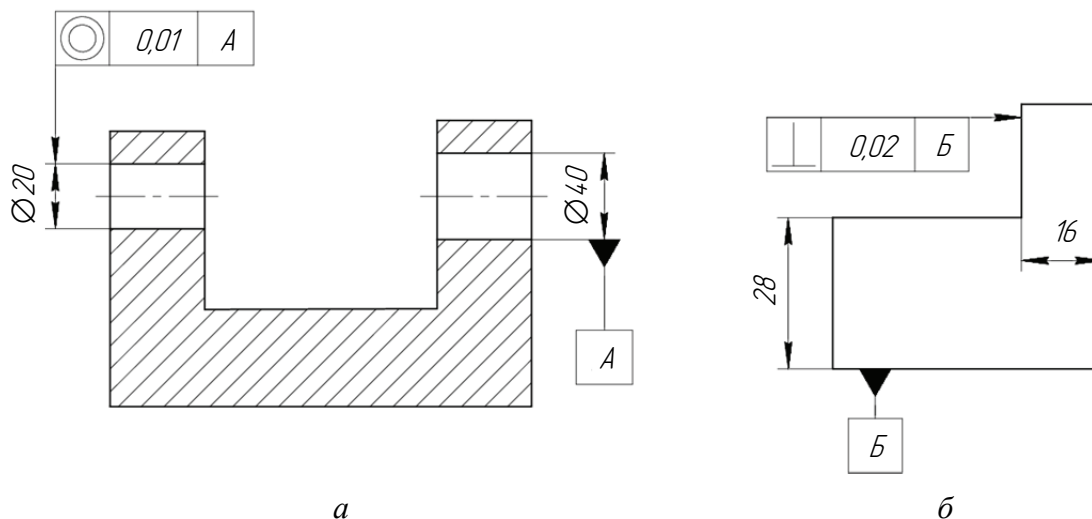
Примеры обозначения допусков расположения:
